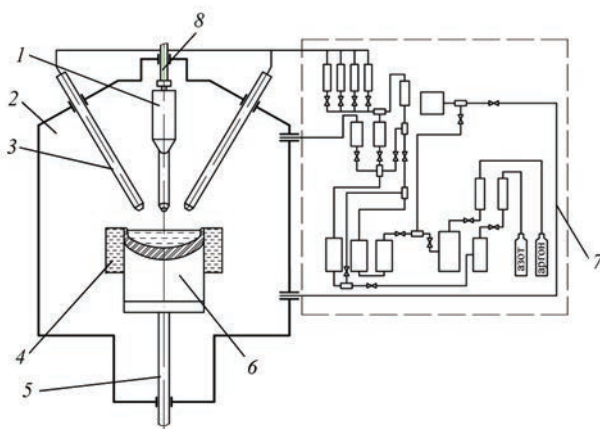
Принципова схема плазмово-дугової печі УПП-3 з системою газоочистки: 1 — витратна заготовка; 2 — плавильна камера; 3 — плазмотрон; 4 — кристалізатор; 5 — механізм витягування зливки; 6 — зливок; 7 — система газоочистки; 8 — механізм подачі витратної заготовки
